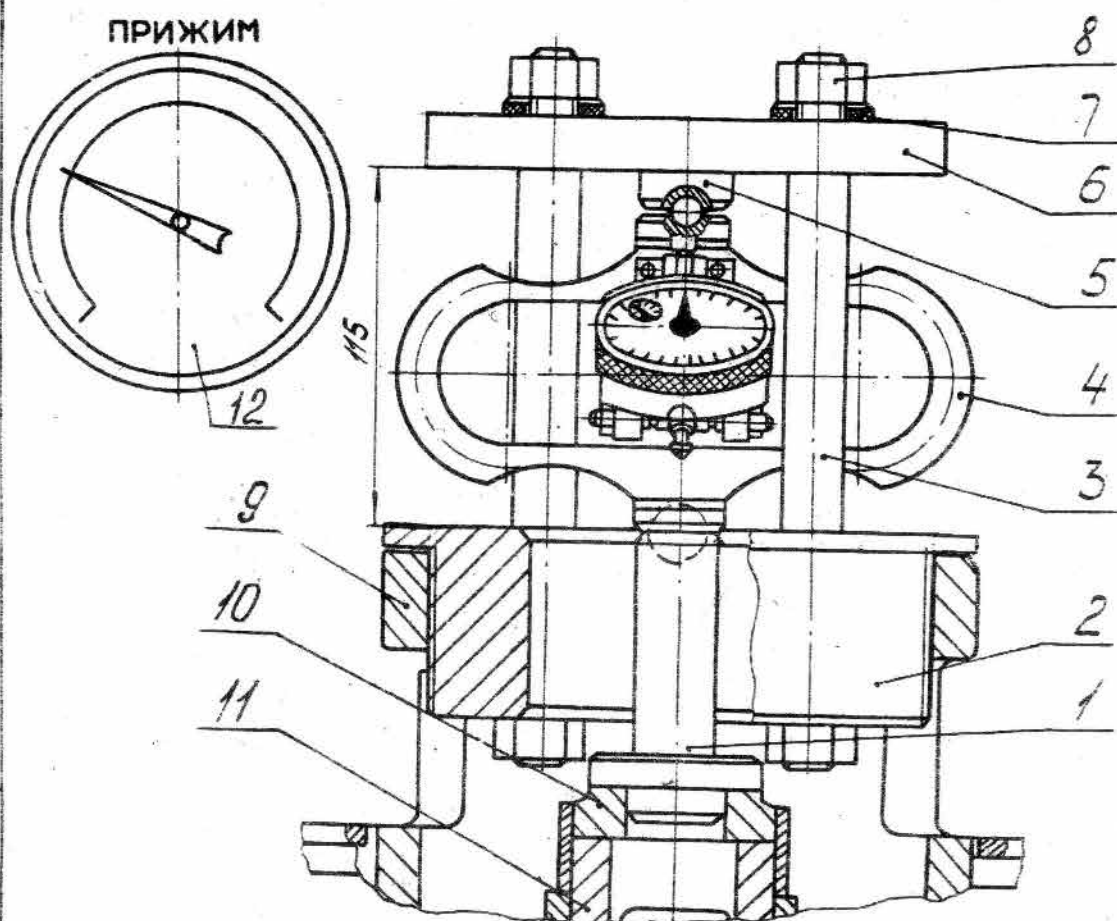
Схема установки приспособления для проверки силоизмерителя прижима
